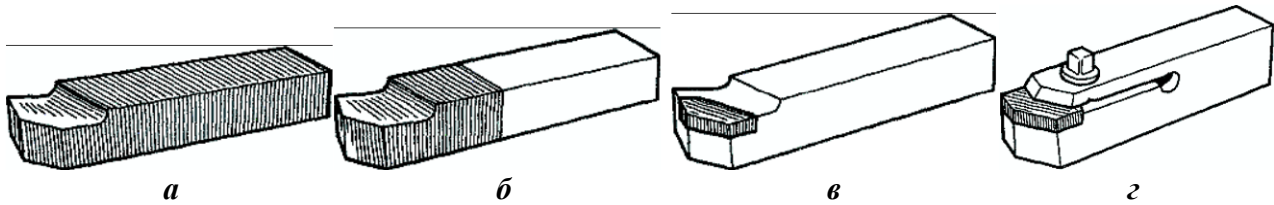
Різновиди різців за способом кріплення робочої частини:
